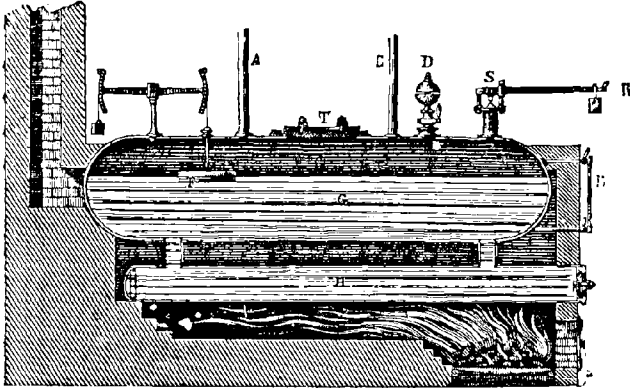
Coupe verticale d'une chaudière à vapeur.
